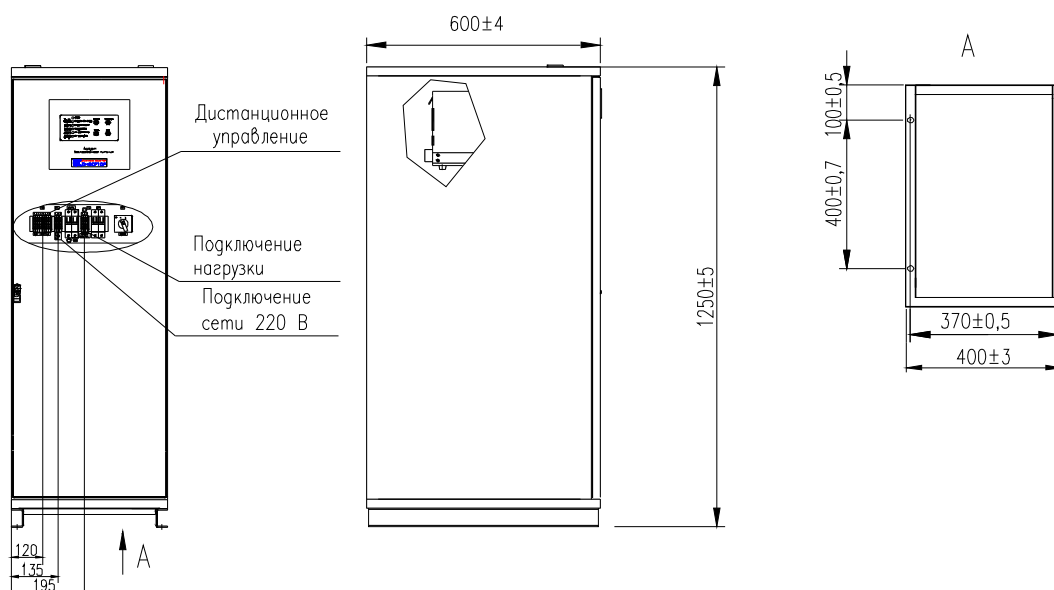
Габаритный чертеж АБП-ООПТ-4.
